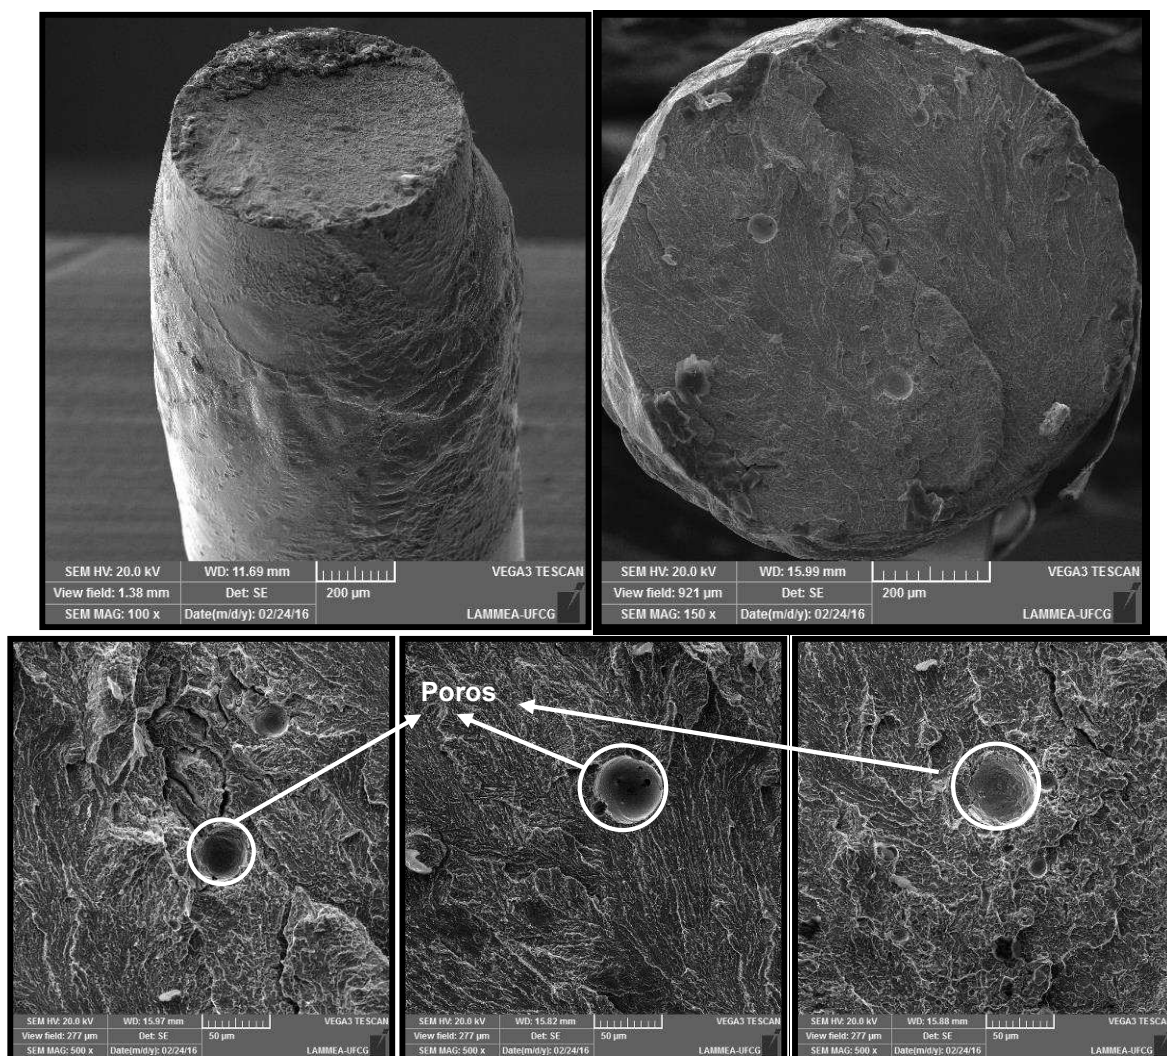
Superfície de fratura da junta dissimilar soldada na configuração 7ms/70% e submetido a ruptura a 40°C.
